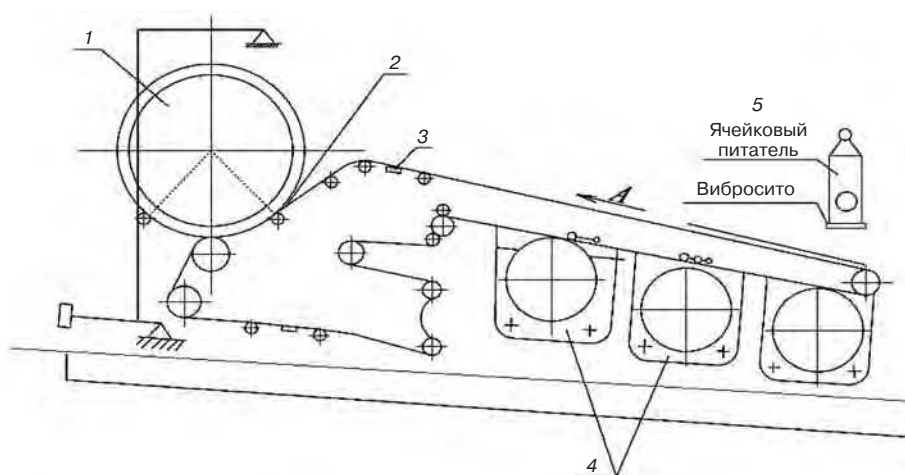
Расположение ячейкового питателя и вибросита над ЛФМ: 1 – форматный барабан; 2 – пресс-вал; 3 – вакуум-коробка; 4 – сетчатые цилиндры; 5 – ячейковый питатель красящей смеси
